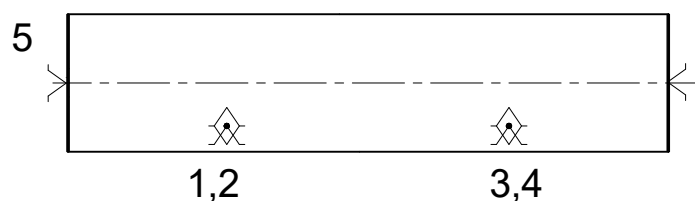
Схема базування на фрезерувально-центрувальній операції
